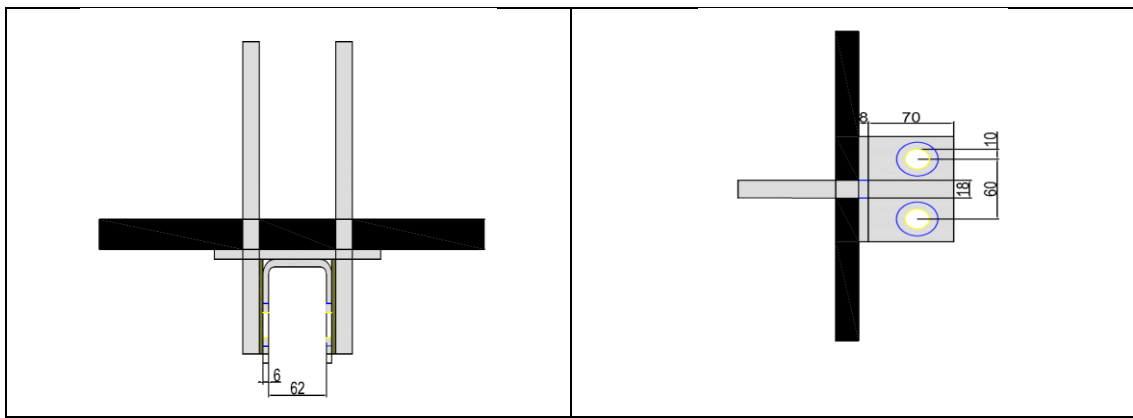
Vista en planta y elevación de estructura de soporte de pesos.
